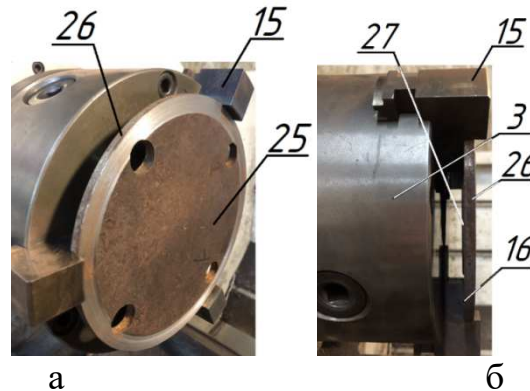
Заготовка «Диск» закрепленная в обратных кулачках – а; с опорой на поверхность обратного кулачка – б.
